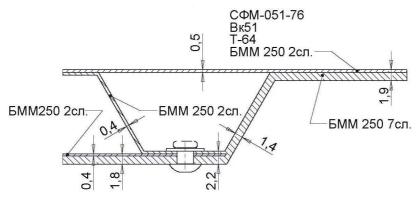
Схема укладки трехслойной конструкции капотов двигательного отсека
